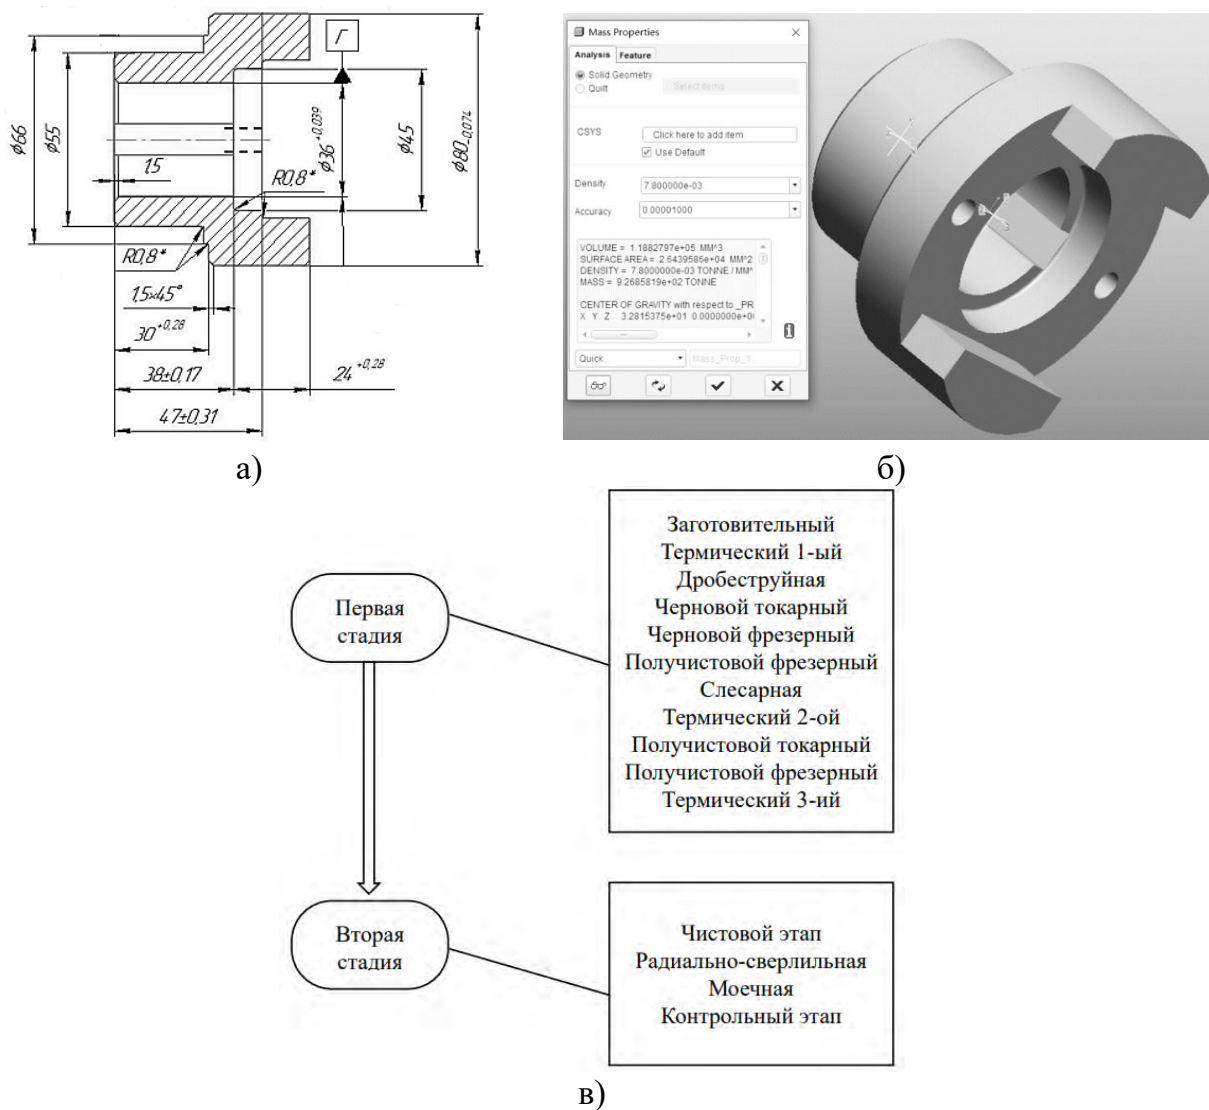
Изготовление полумуфты: а) Чертеж муфты; б) 3D модель; в)технология обработки детали
